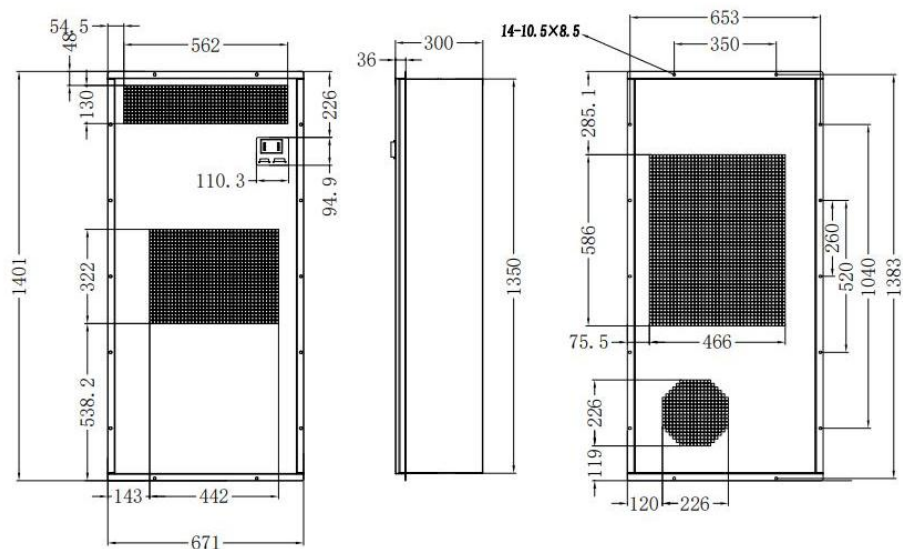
Габаритные размеры SNR-ACC-5000-ACH
